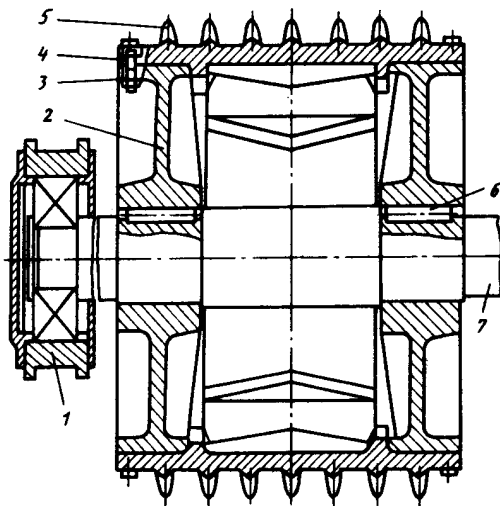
Валок двухвалковой зубчатой дробилки СМД-175А:
